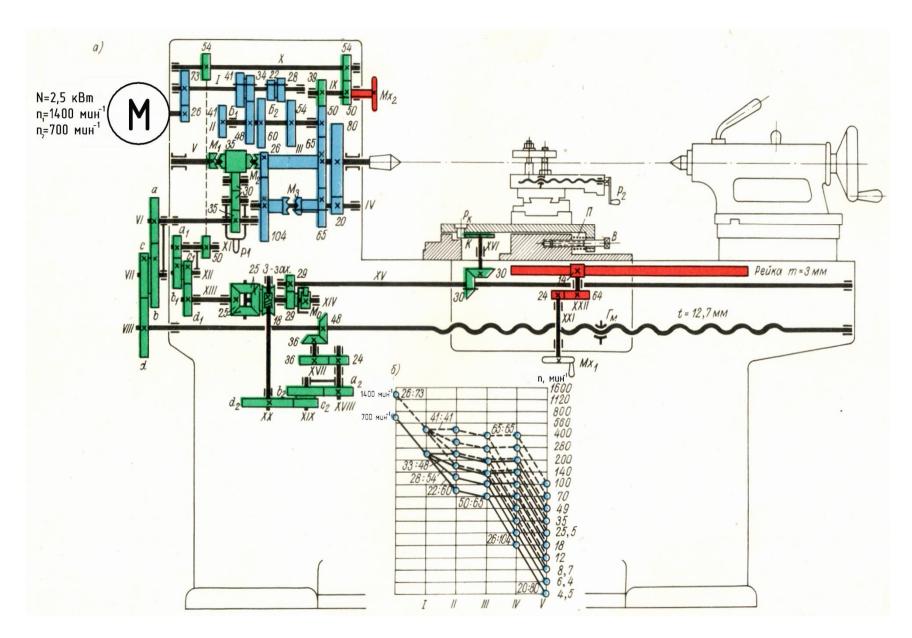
Кинематическая схема токарно-затыловочного станка модели К96
